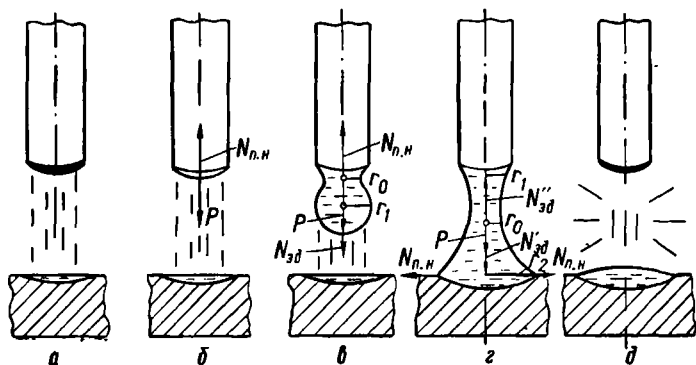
Схема образования капли и переноса ее в сварочную ванну.
